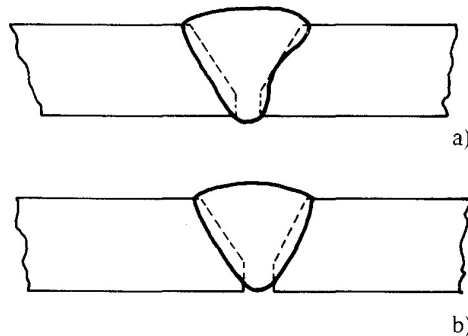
Falta de fusão, a) no flanco, b) na raiz da junta soldada.
